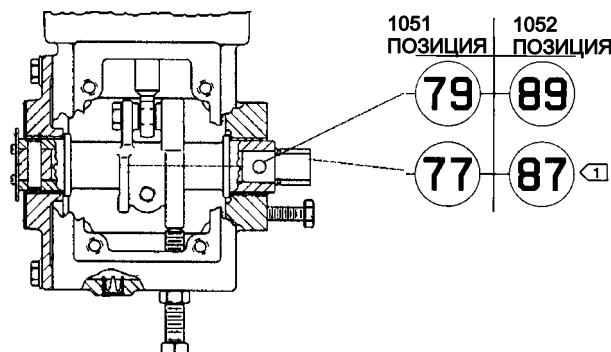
Привод Fisher модели 1052 размера 33, типы крепления F и G
